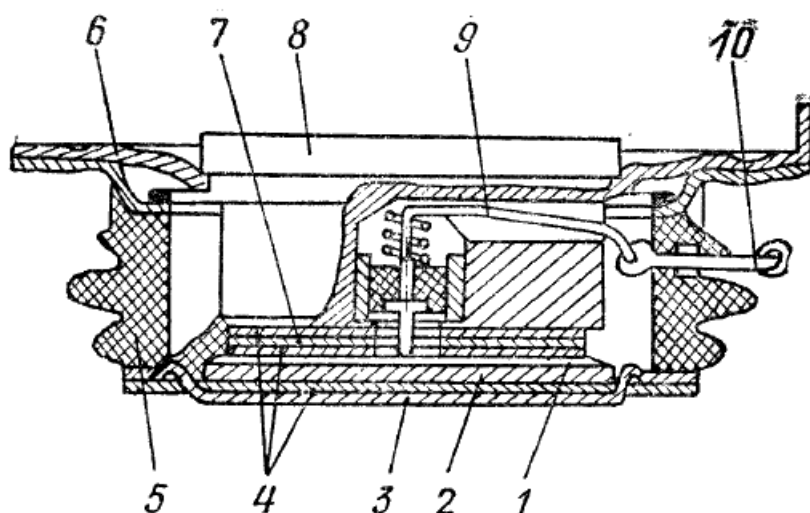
Конструкция таблеточного тиристора T500: 1 – Кремниевый диск; 2 – Термокомпенсирующий электрод из вольфрама; 3 – Медная мембрана; 4 – Прокладки; 5 – Керамический корпус; 6 – Манжета; 7 – Второй термокомпенсирующий диск из молибдена; 8 – Кремниевый диск; 9 – Внутренний управляющий вывод; 10 – Внешний управляющий вывод
